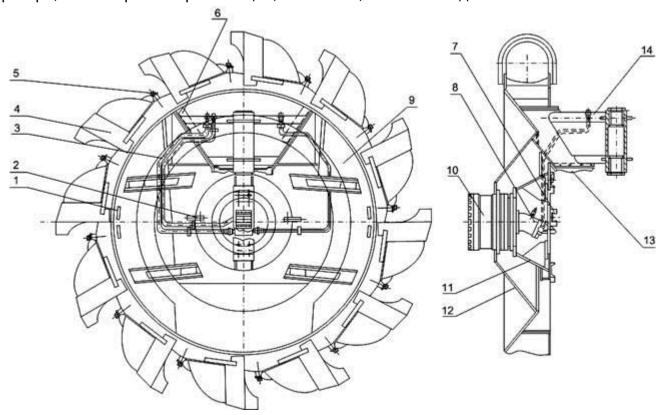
Ротор: 1 -крюк; 2 -проушина; 3 -трубопроводы; 4 -ковш; 5 -болт; 6 -нож; 7 -направляющая; 8 -гидромотор; 9 -подковшовый кожух; 10 -редуктор; 11 -корпус; 12 -роторное колесо; 13 -кожух резиновый; 14 -кронштейн
